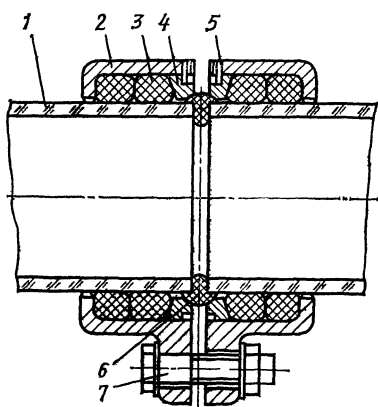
Соединение стеклянных труб с гладкими концами:
